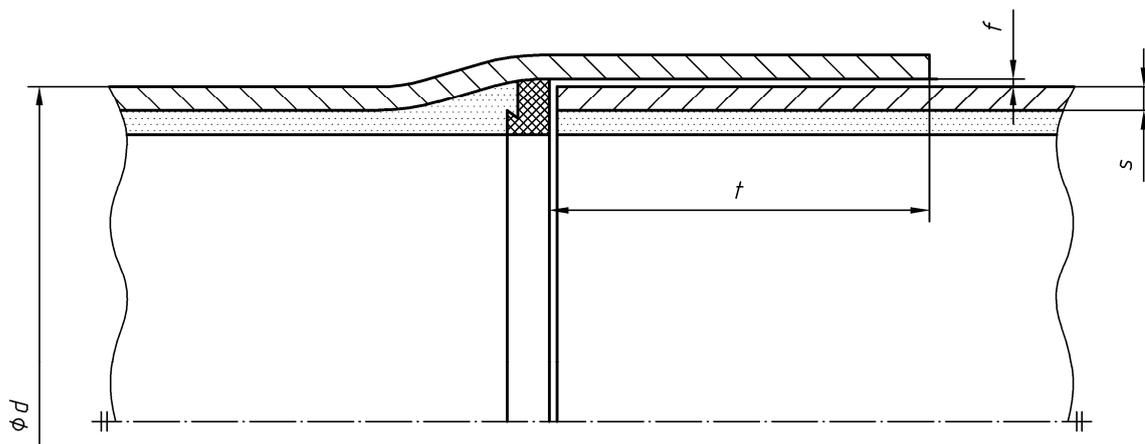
Einsteckschweißmuffenverbindung
